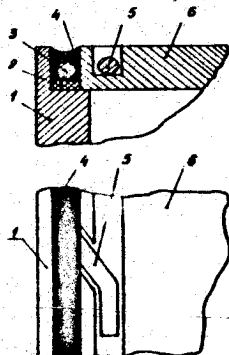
Герметизація корпусу блока мікроелектронної апаратури: 1- корпус; 2- гумова прокладка; 3- лужений дріт; 4- припій; 5- вільний кінець дроту; 6- кришка
